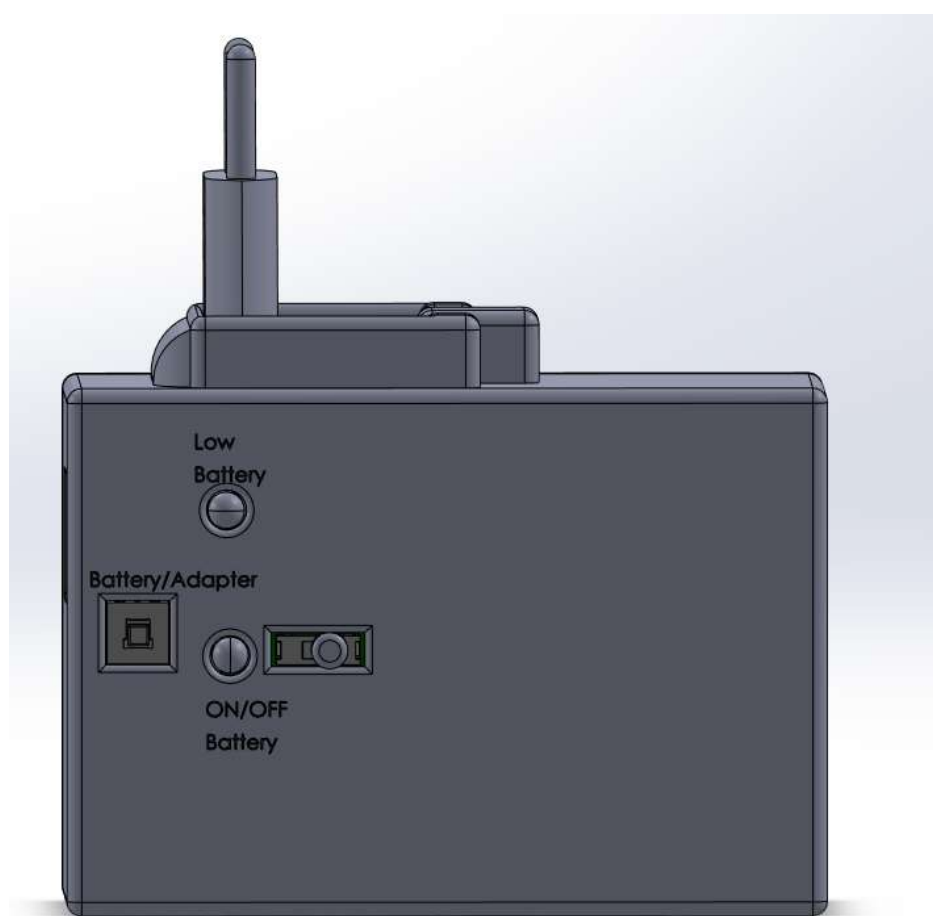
Вигляд корпусу спереду та з піднятою вилкою зарядки
